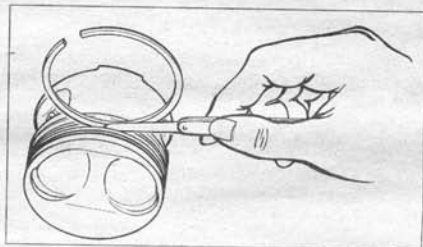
Проверка зазора между поршневыми кольцами и канавками
